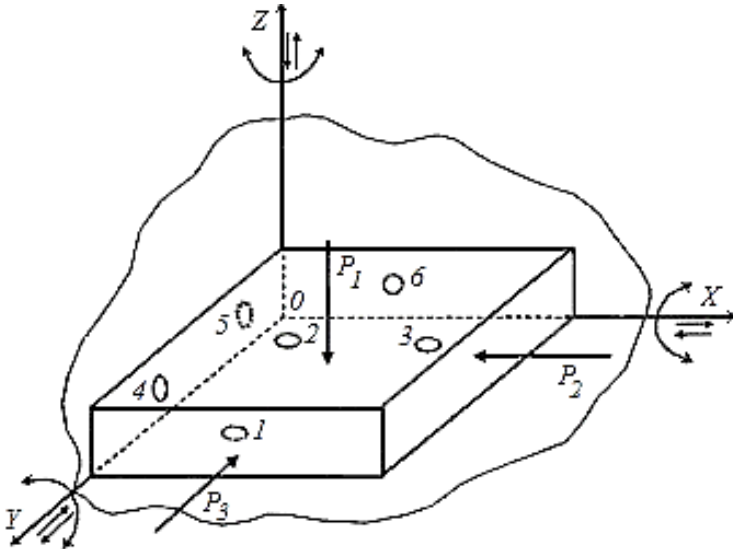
Схема базування та закріплення призматичної деталі [4]
